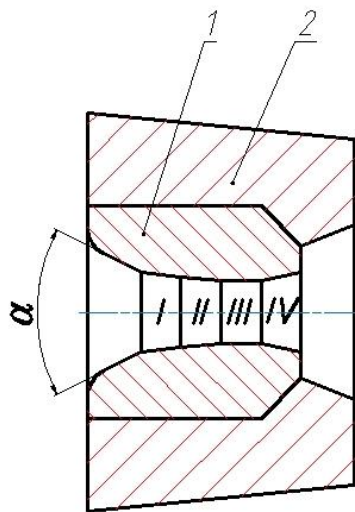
Загальний вигляд волоки: 1 – волока; 2 – обойма.
